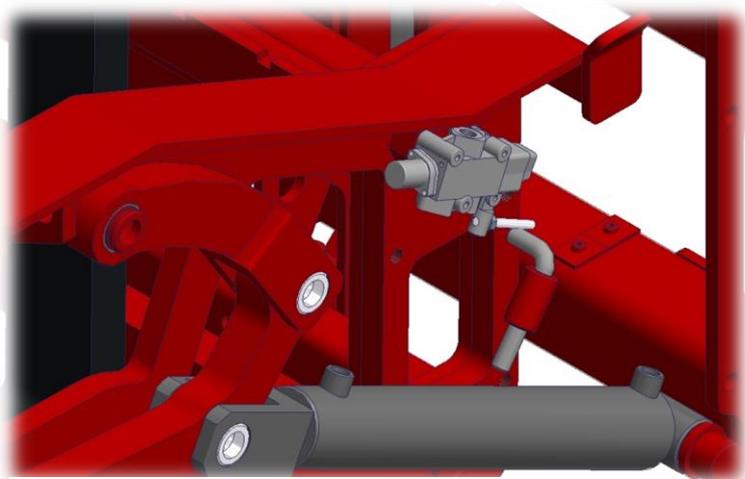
Hydraulischen Endanschlags/Schalters
